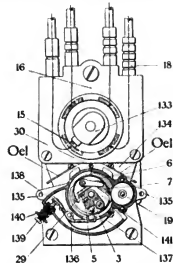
Stirnansicht des Magnetinduktors der Bosch-Doppelzündung.
